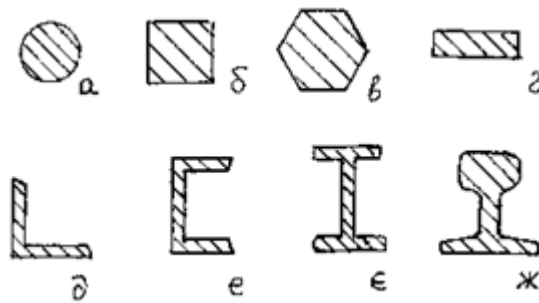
Сортовий прокат: а – круг; б – квадрат; в – шестигранник; г – штаба; д – кутова сталь; е – швелер; є – двотавр; ж – рейка
